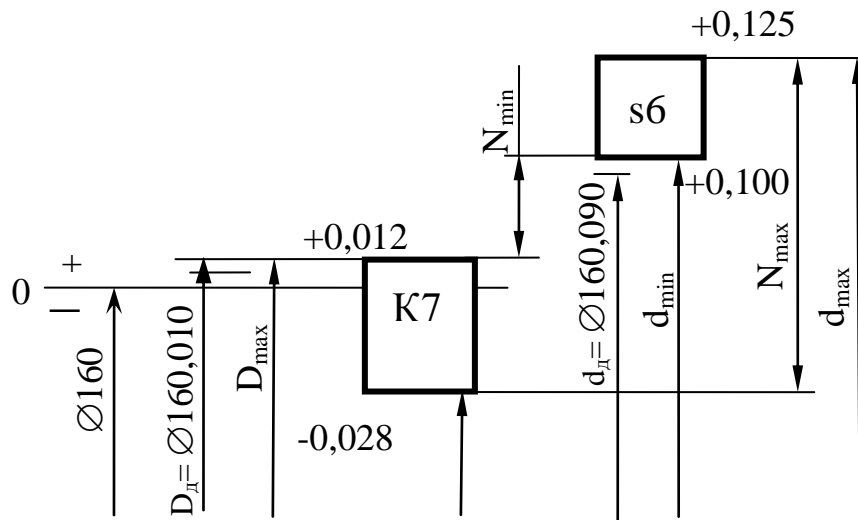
Схема розташування полів допусків з'єднання Ø160 K7 / s6
